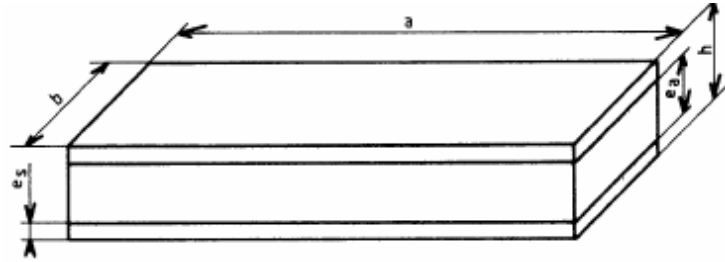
Représentation d'un sandwich (deux peaux et une âme).
